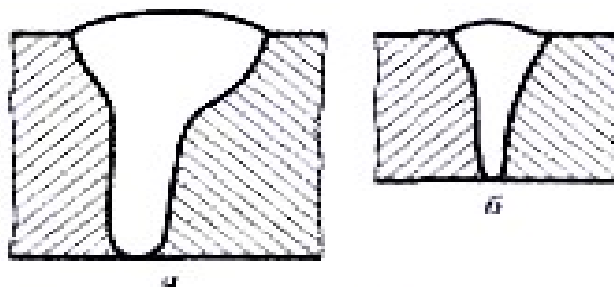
Форма шва в поперечном сечении при лазерной сварке стали:
